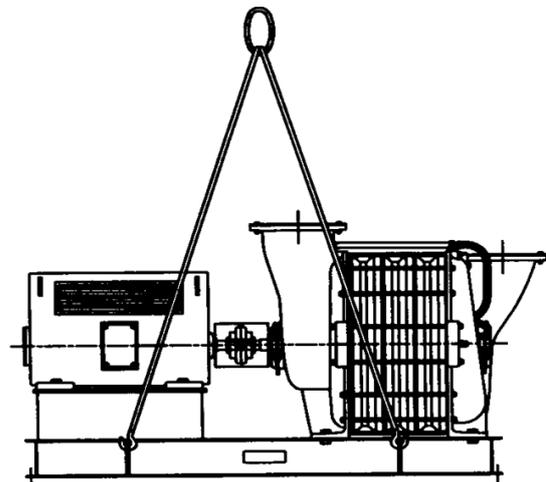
Fissare il mezzo di sollevamento al gruppo macchina con golfari
